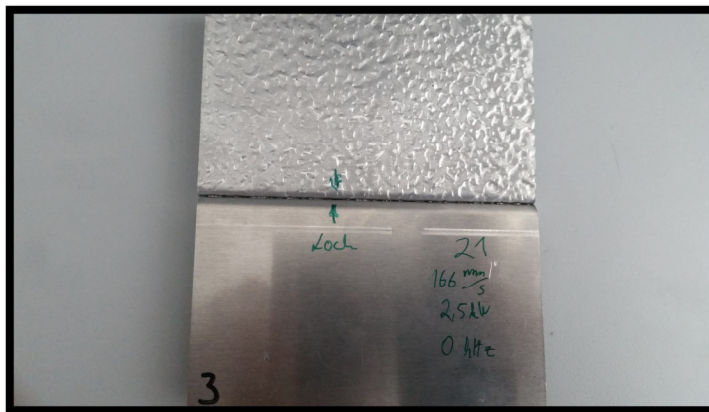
Nahtfehler undichte Schweißnaht
